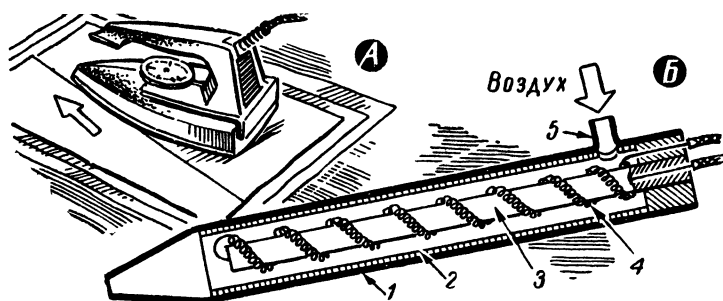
Инструмент для сварки пленок: А — утюг; Б — устройство для получения горячего воздуха: 1 — трубка; 2 — слюда; 3 — фарфоровый стержень; 4 — спираль; 5 — отросток.
